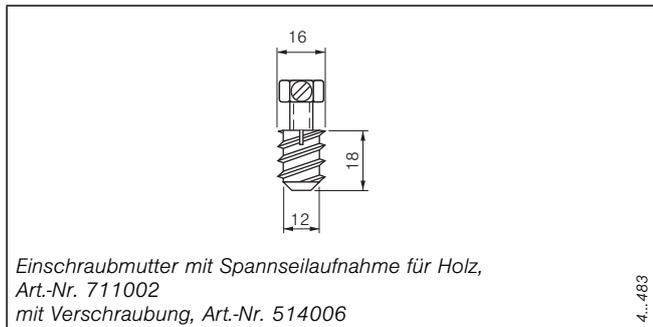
Einschraubmutter mit Spannseilaufnahme für Holz
